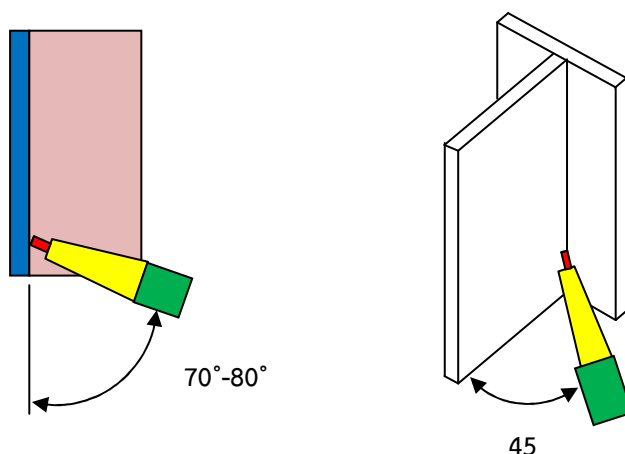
การเชื่อมท่าขนานนอน (Horizontal Welding) 2F
